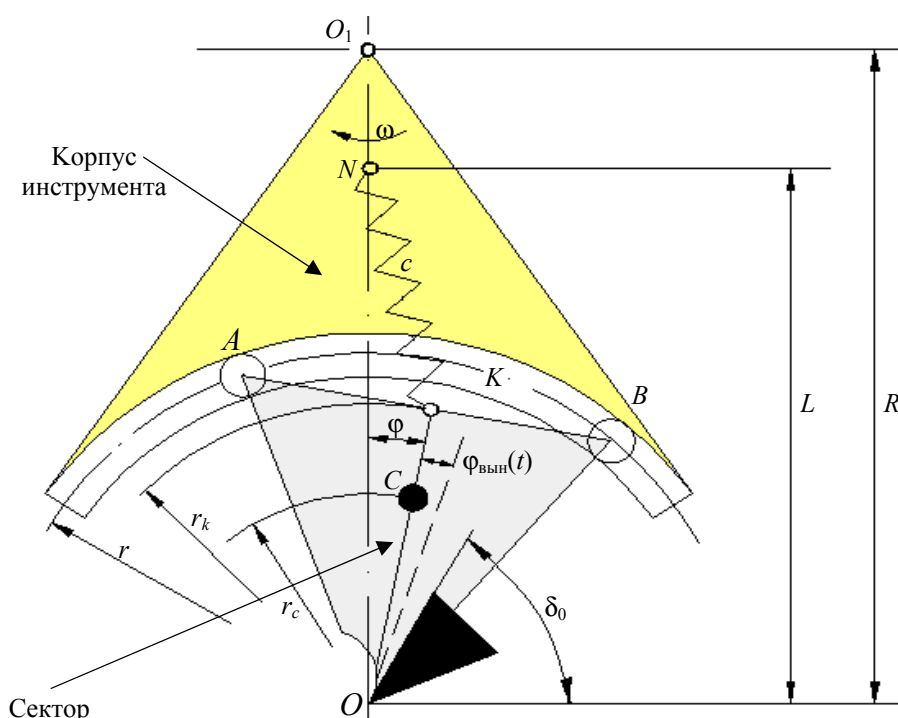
Расчетная схема фрезерного инструмента с изменяемыми углами резания
